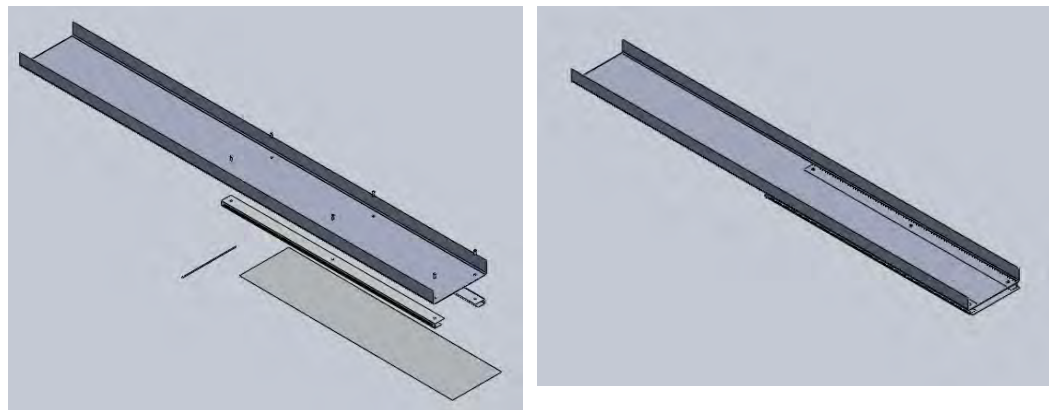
a) Explosivo del subensamble del canal exterior.
